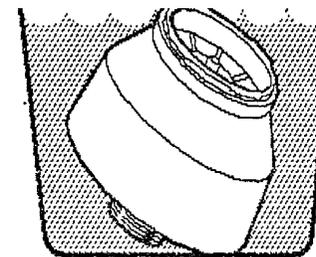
Мойка корпуса (VRM и VRR) регуляторов
